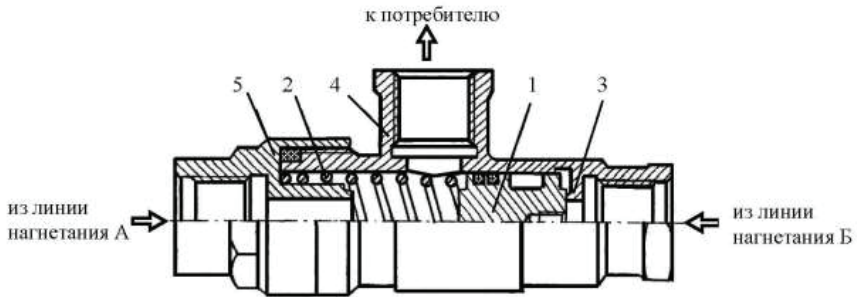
Принципиальная схема челночного клапана, где 1- шток; 2- пружина; 3- седло; 4- корпус; 5- штуцер
